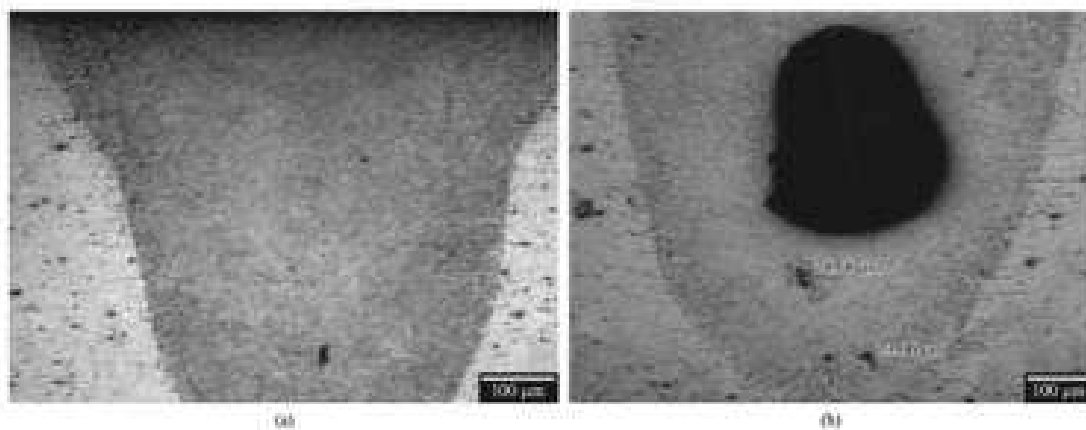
Газовые поры в сварном шве
